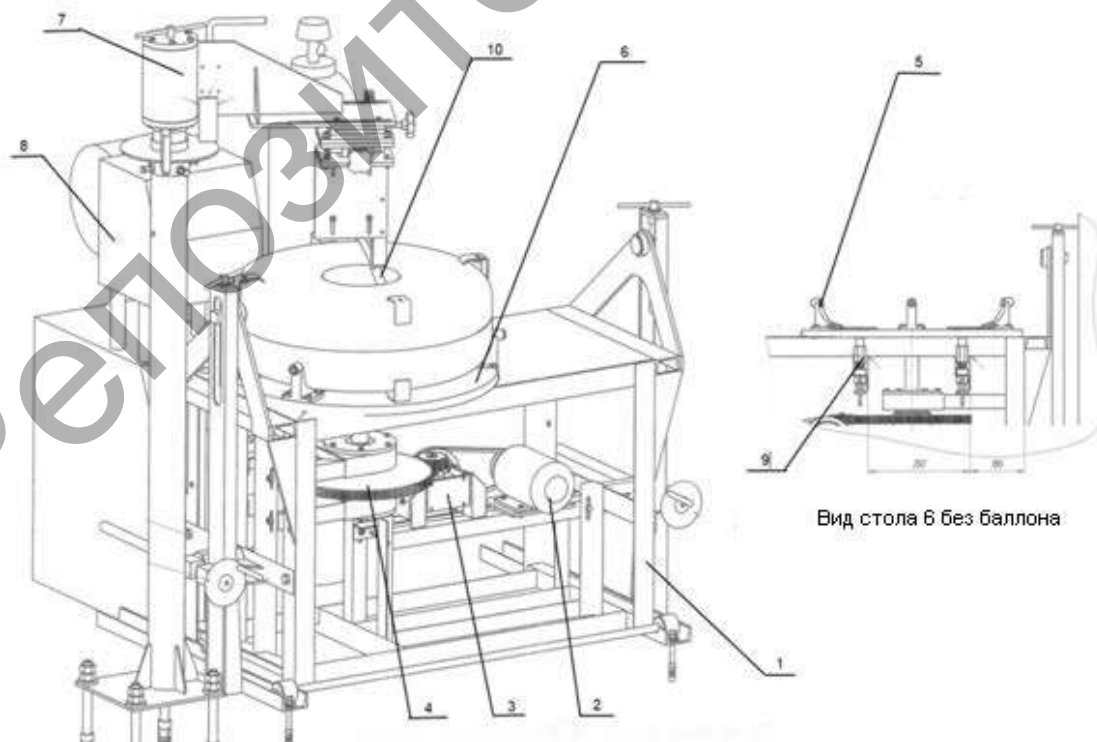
Общий вид стенда для сварки центрального днища
